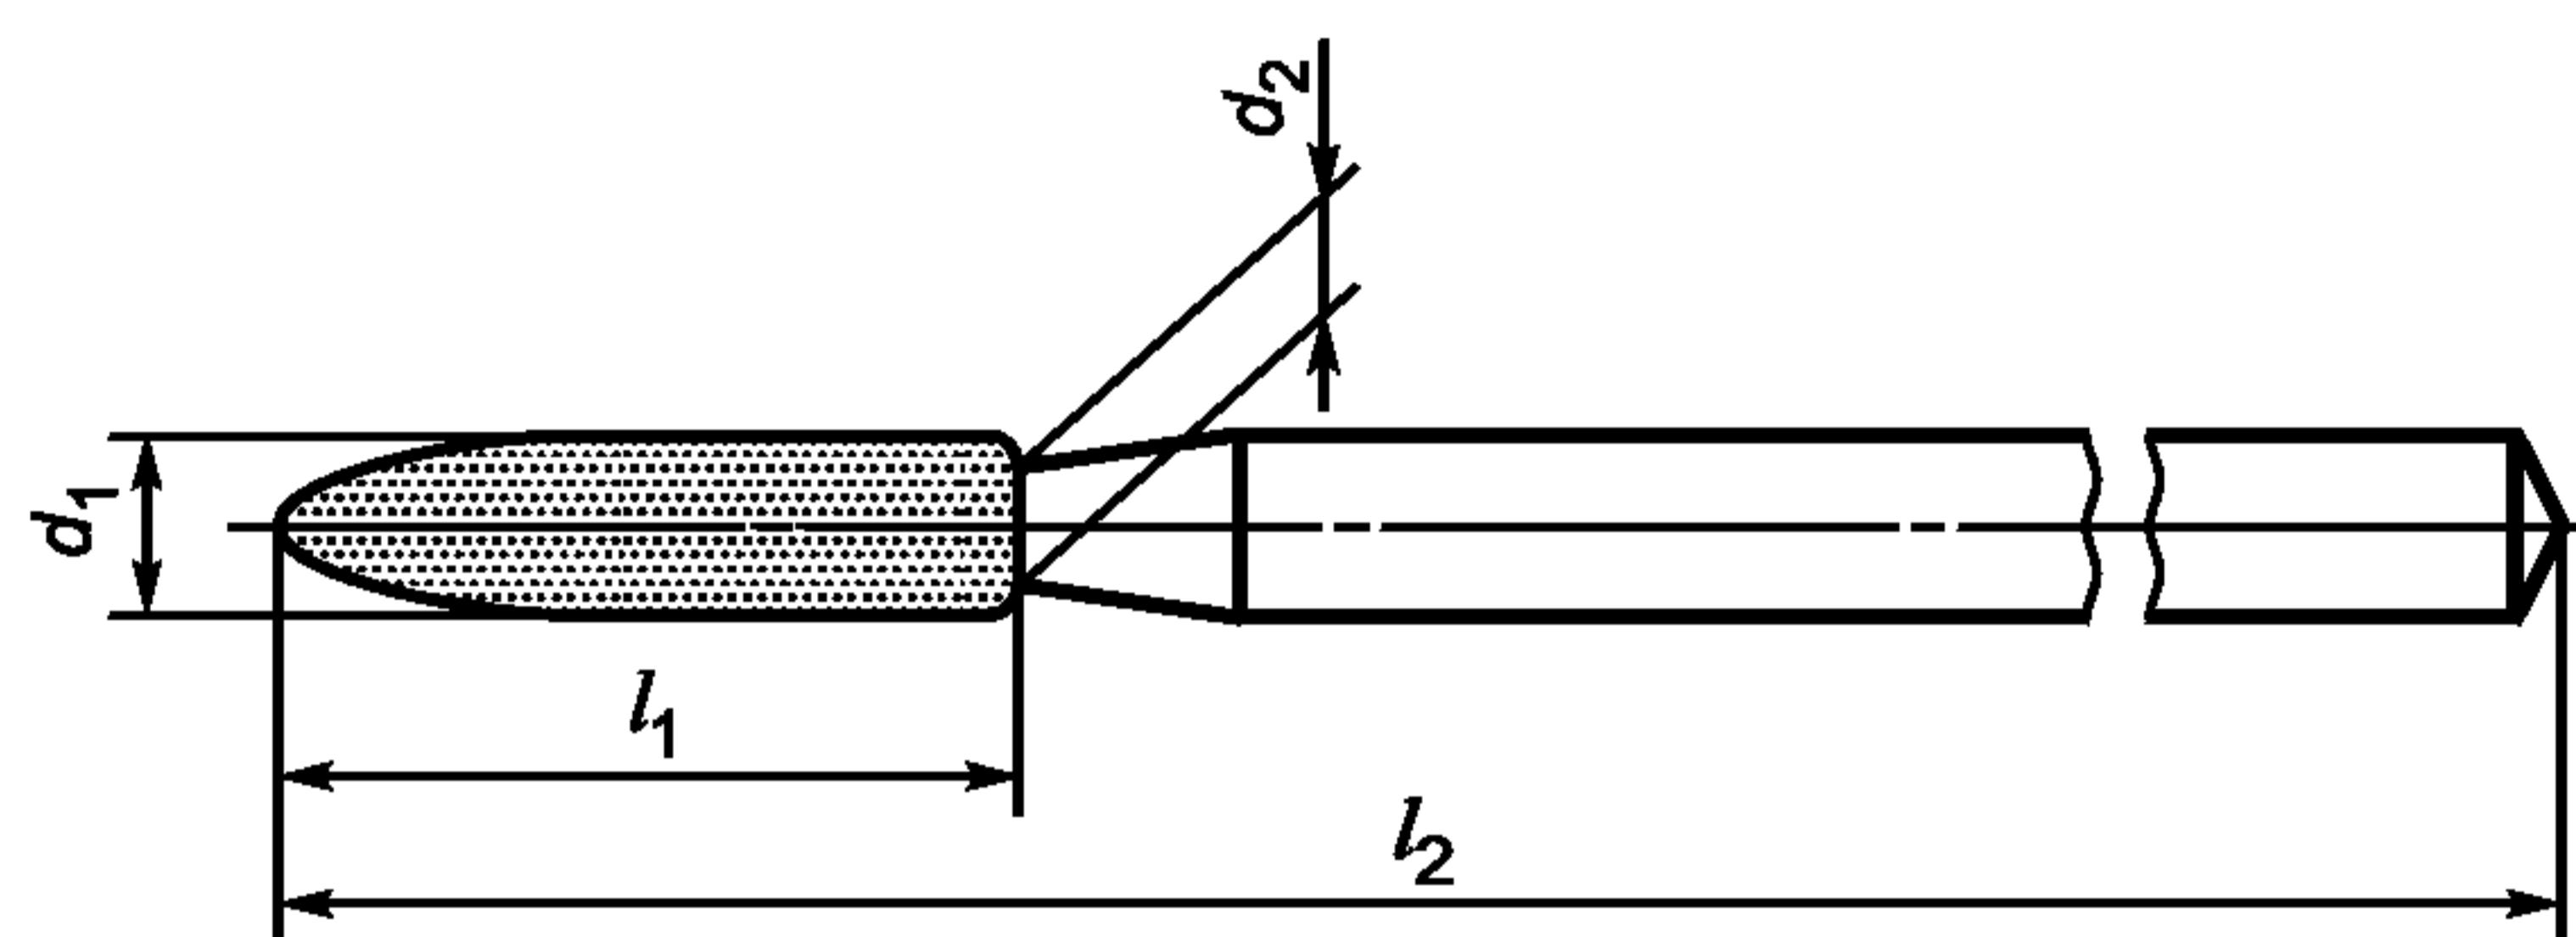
Цилиндрическая с огивальным концом рабочая часть с длиной головки 6,0 мм
